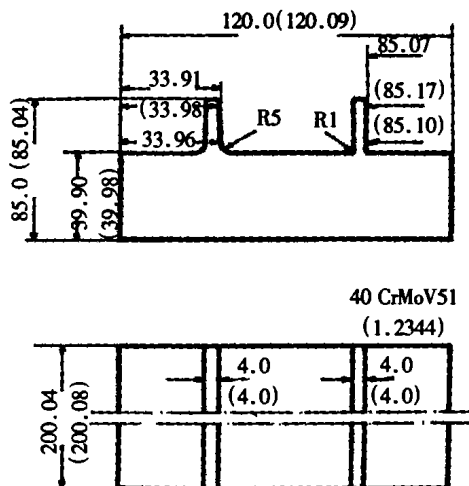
典型结构之测试模具, 括号内尺寸为气淬后尺寸(单位: mm)
